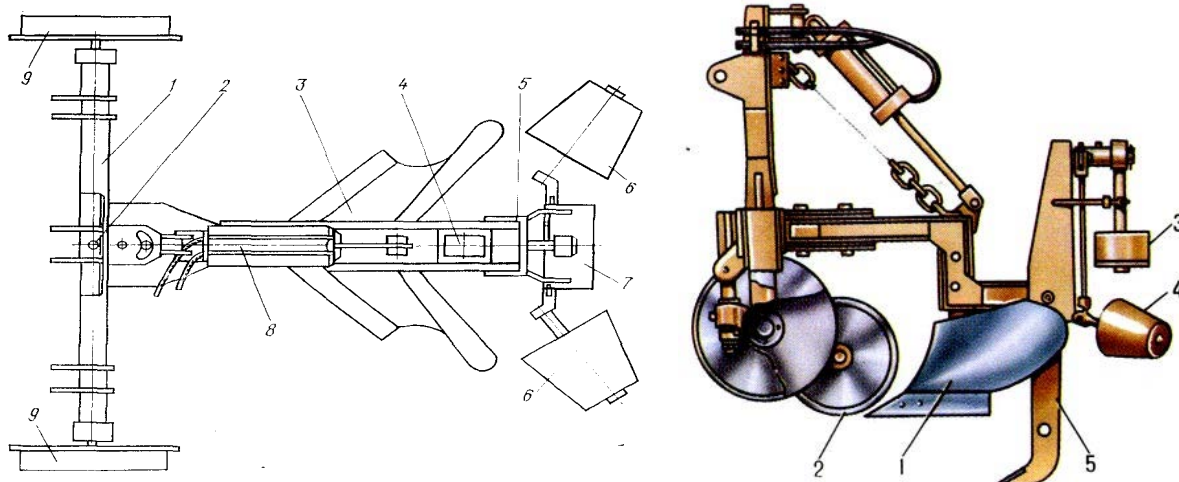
Плуг для склонов ПЛС-0,6 (вид сверху): 1 — рама; 2 — дисковый нож; 3 — двухотвальный корпус; 4 — рыхлительная лапа; 5 — приспособление для прикатывания пластов; 6 — прикатывающий ролик; 7 — груз; 8 — выносной гидроцилиндр; 9 — опорные колеса
